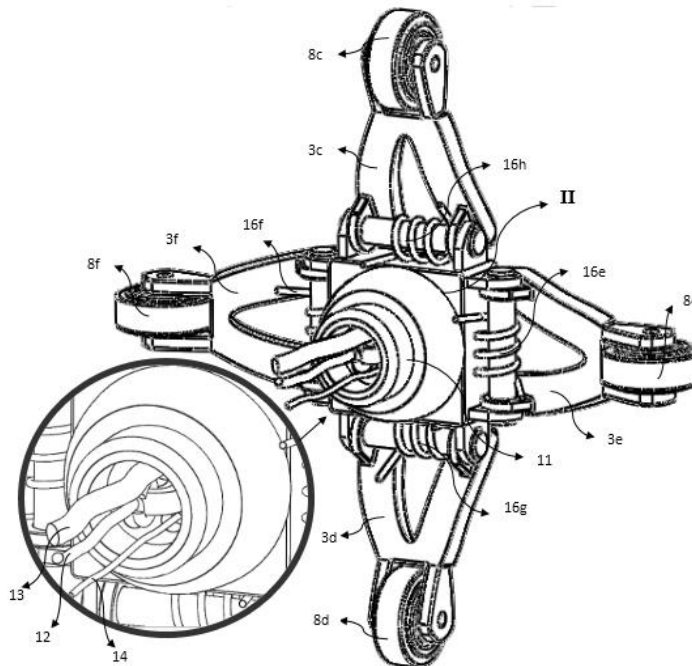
Diseño CAD del robot. Sección trasera II. (Vista isométrica)
